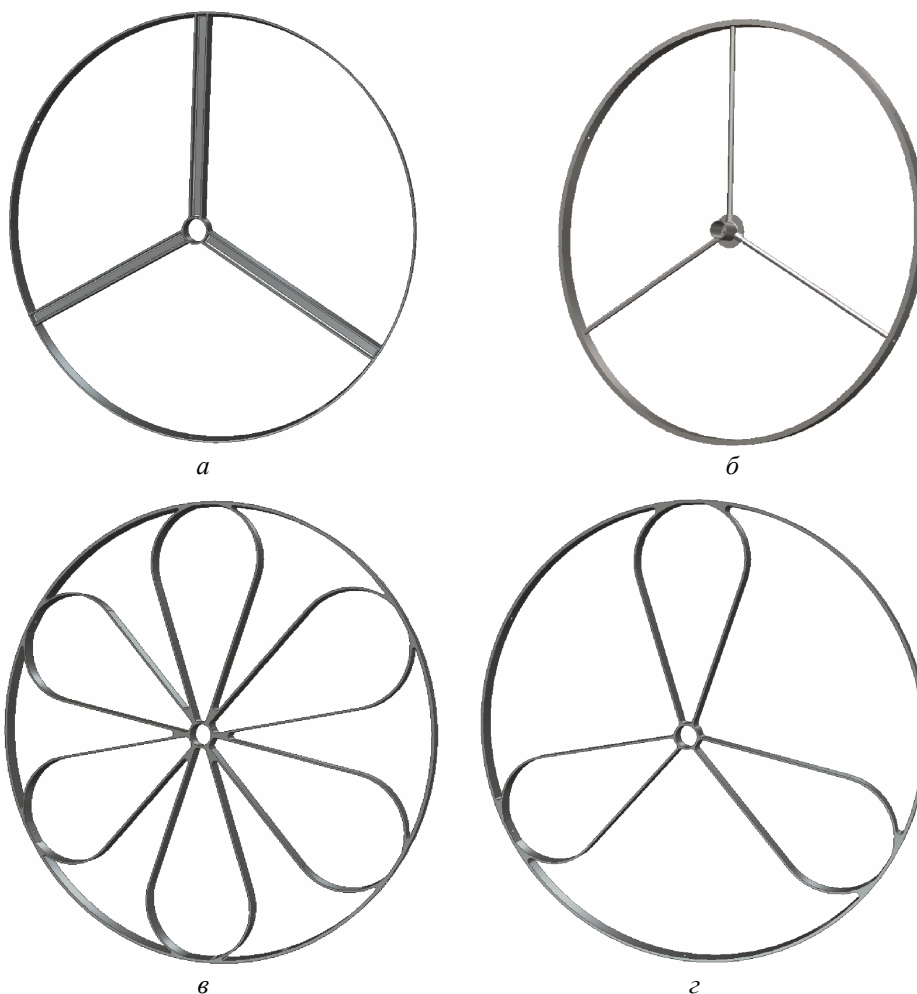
Крепежные конструкции с использованием: а — двутавров; б — круглых стержней; в, г — профилей прямоугольного сечения
